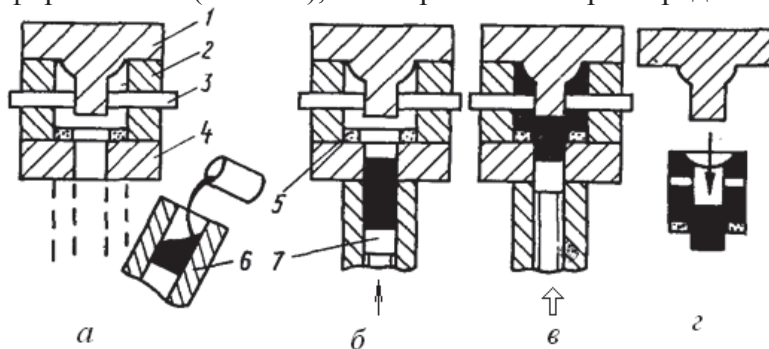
Изготовление поршней способом ЛКД на литейной машине с нижним узлом прессования: а – заливка металлического расплава в металлоприемник; б – начало вытеснения расплава из металлоприемника в матрицу; в – уплотнение затвердевающей отливки; г – сьем отливки с верхней полуформы; 1, 2, 4 – детали пресс-формы; 3 – стержень; 5 – керамическая вставка; 6 – металлоприемник; 7 – пуансон (плунжер)
